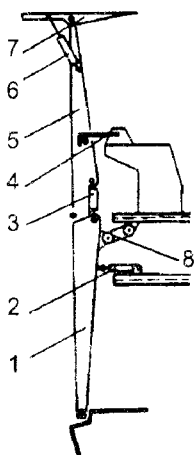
Схема устройства кормовой угловой аппарели.
